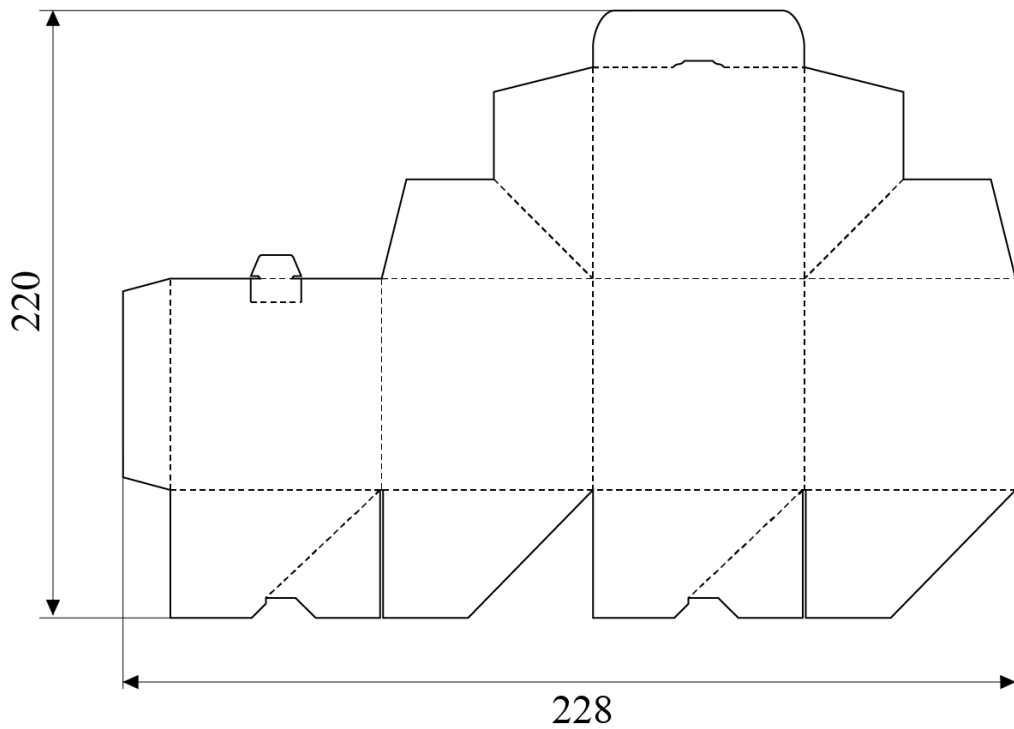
Розгортка середньої подарункової упаковки
